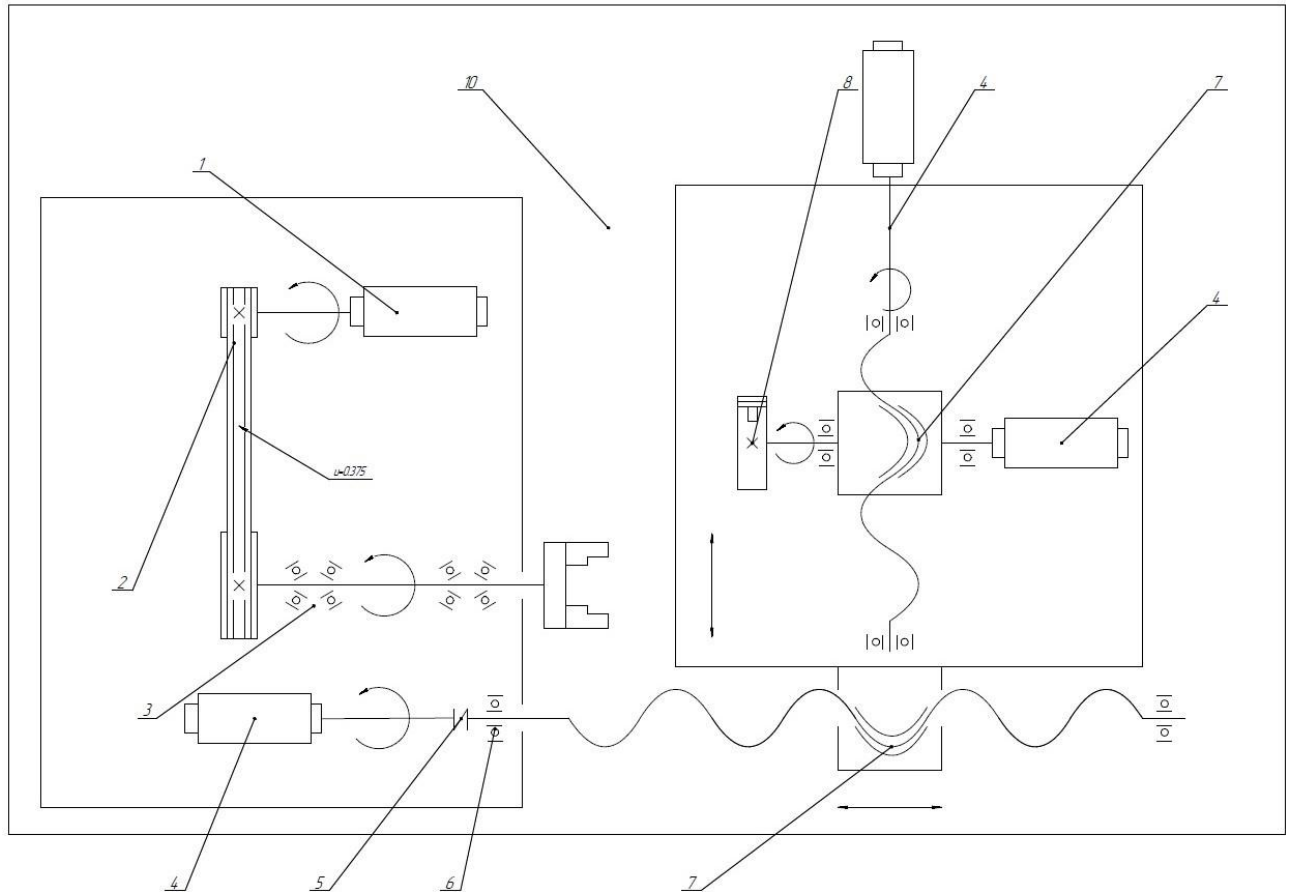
Принципиальная кинематическая схема настольного токарно – револьверного станка с ЧПУ
